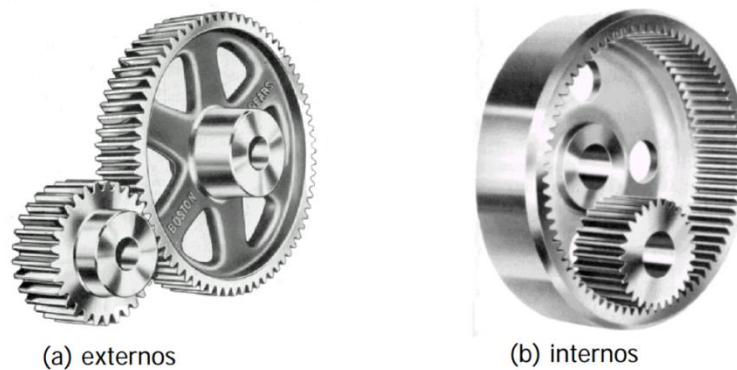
(a) Engranaje cilíndrico de dientes rectos externo. (b) Engranaje cilíndrico de dientes rectos interno^{xix}.
